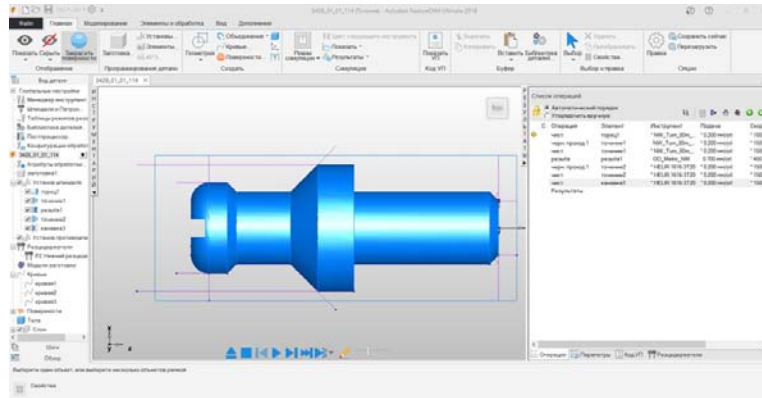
Импорт твердотельной модели детали и назначение профиля заготовки
